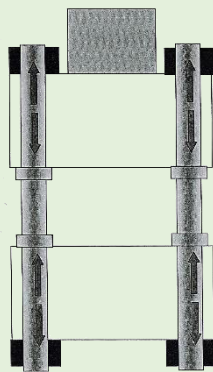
Estructura en columnas de prensas de fricción e hidráulicas de bajo tonelaje. Imagen: SACMI.
